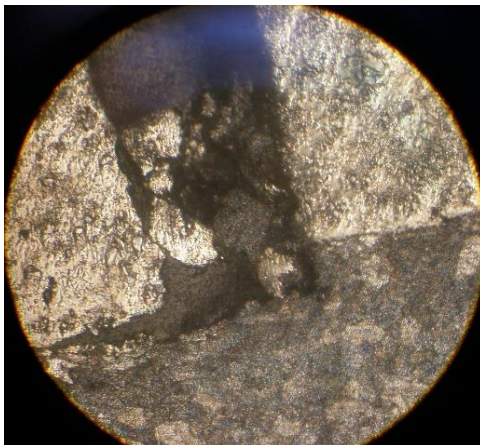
Тріщина при деформуванні заготовки з покриттям
